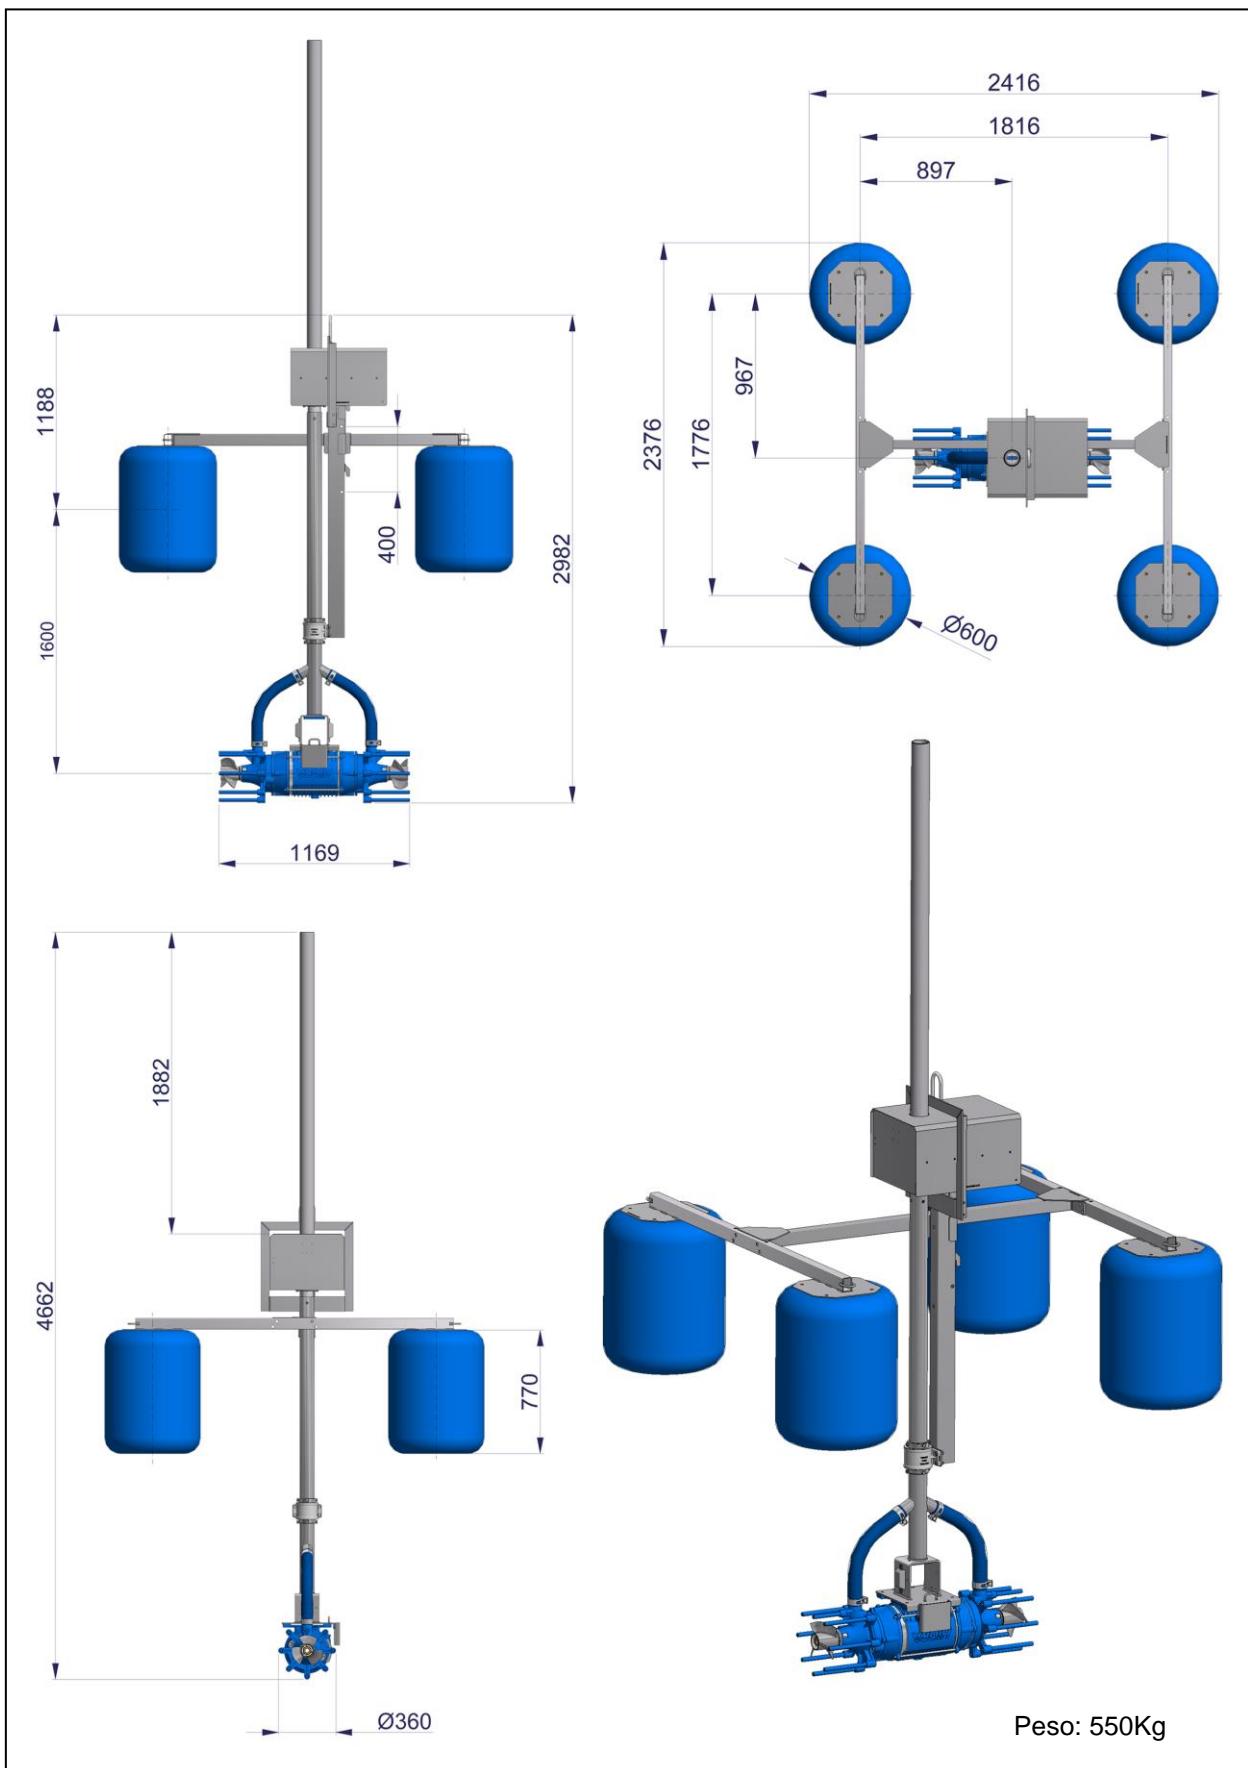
Dimensional TORNADO-R BITURBO 25,30 e 40CV
